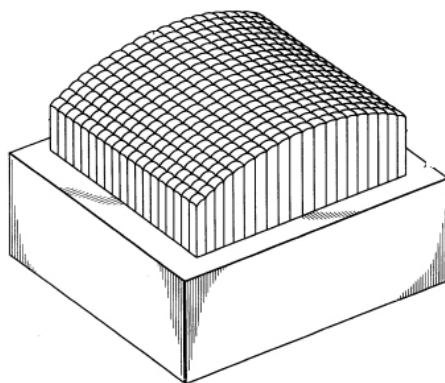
Schema instalației de deformare prin tragere pe poanson cu suprafețe discrete
